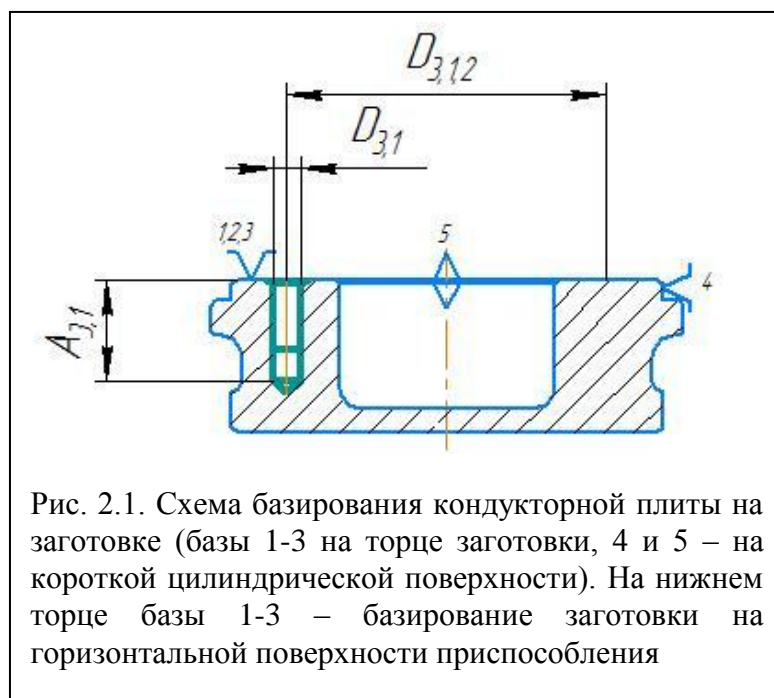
Схема базирования кондукторной плиты на заготовке (базы 1-3 на торце заготовки, 4 и 5 – на короткой цилиндрической поверхности). На нижнем торце базы 1-3 – базирование заготовки на горизонтальной поверхности приспособления
